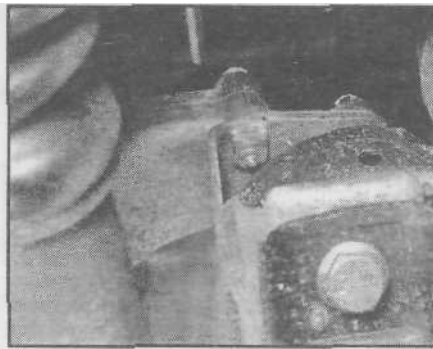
Правая задняя опора двигателя (вид снизу) - 1, 8 литра
